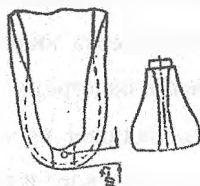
Установка пяточной части заготовки верха обуви на колодке
